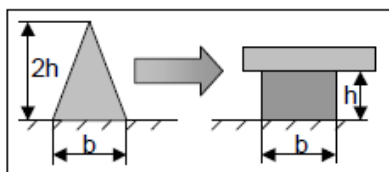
Comprimere il cordone adesivo fino alla dimensione
